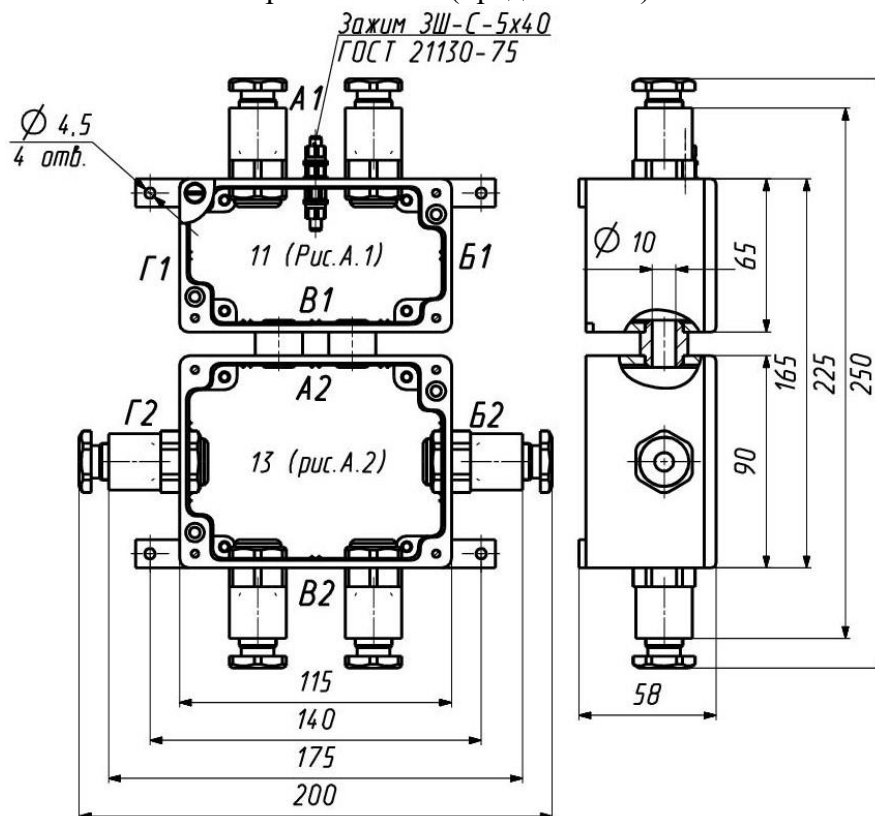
Блок корпусов и коробка клеммная ЕхБКО-А11В1/А13А2 (скрепление корпусов типоразмеров 11 и 13 сторонами В1 и А2) – вариант 5
